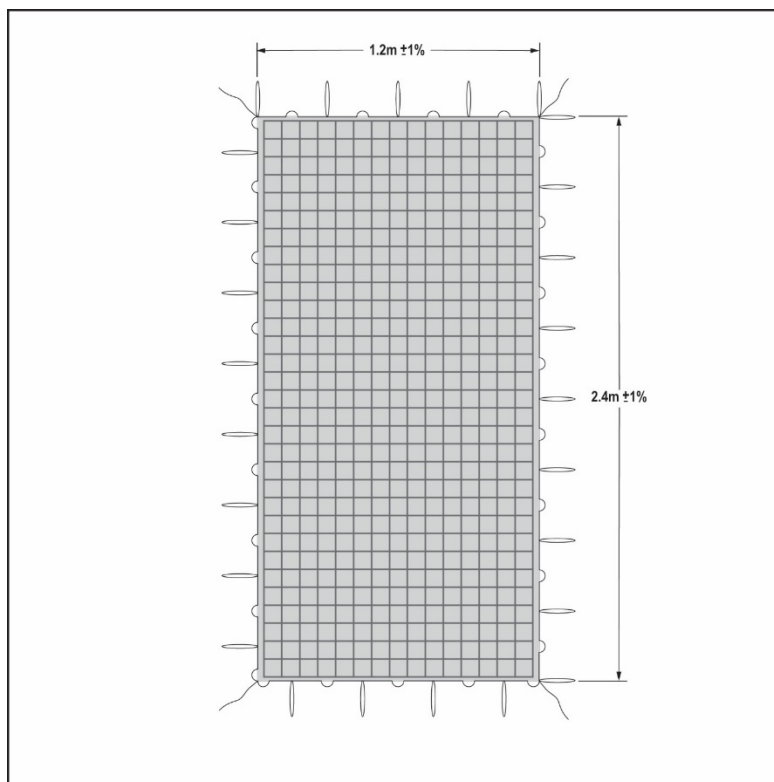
Schéma d'un EITE de 2,4 m sur 1,2 m
